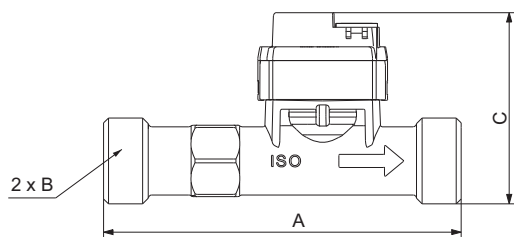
Размеры, VFS QT, 2-40 л/мин, резьбовые соединения
